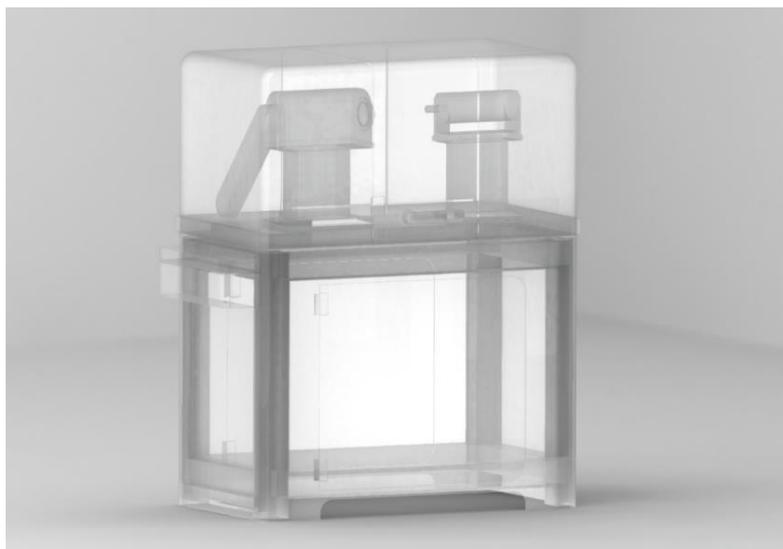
Размещение общей конструкции корпуса в основании каркаса
